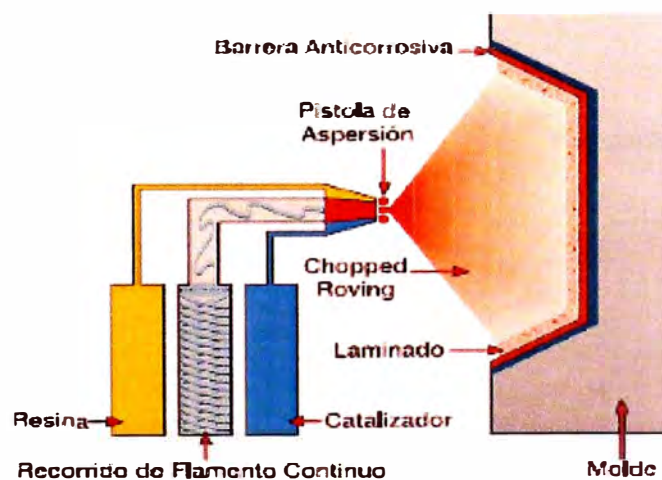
LAMINADO A PISTOLA (SPRAY-UP)
